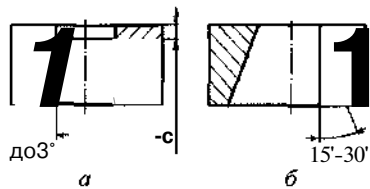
Конструкции матриц для вырубных (пробивных) штампов:
